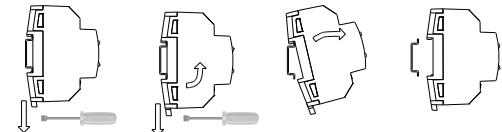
Montaje de IndustrialBOX 4 en carril DIN
